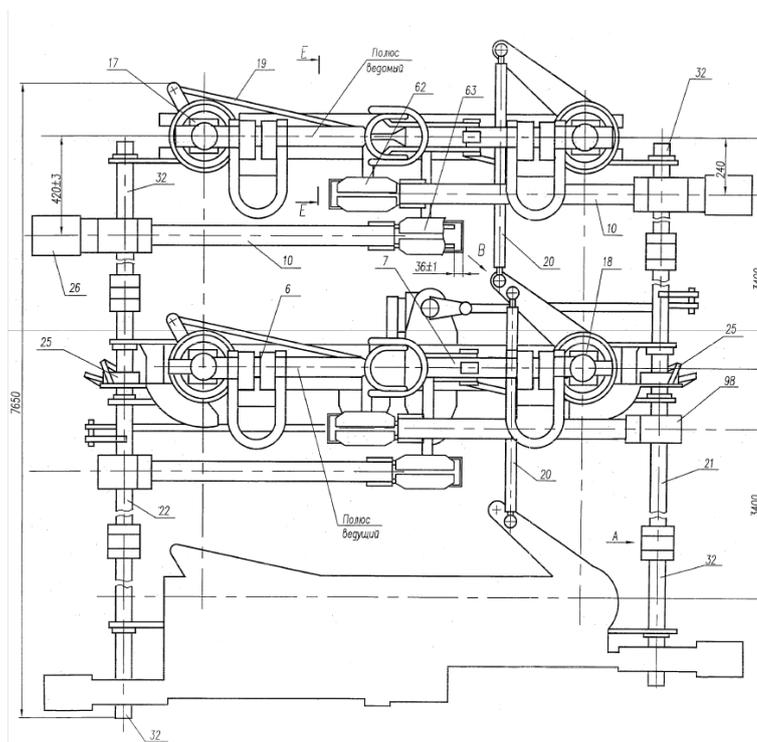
Общий вид РГН.2-220.П/100-40УХЛ1:
